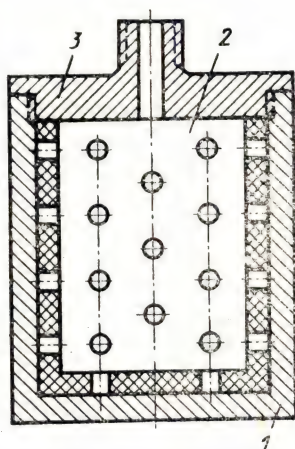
Схема глушителя для сброса воздуха из пнев­моцилиндров:
